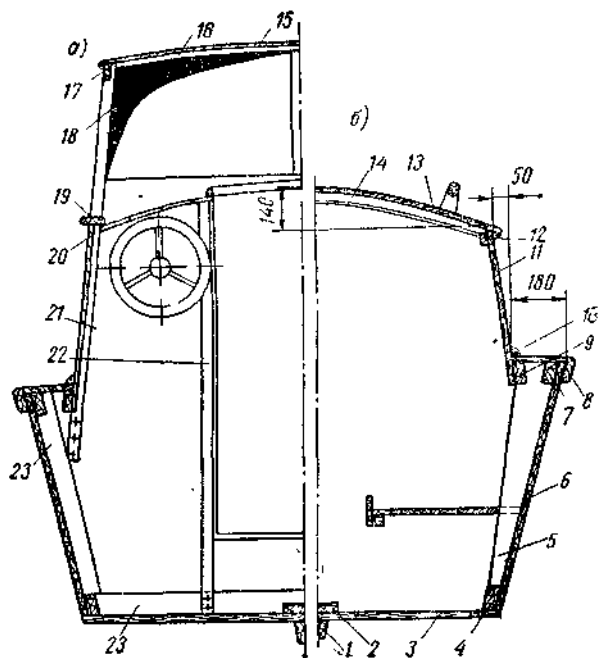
Поперечные сечения корпуса: а — по переборке каюты (см. в нос); б — по каюте.
